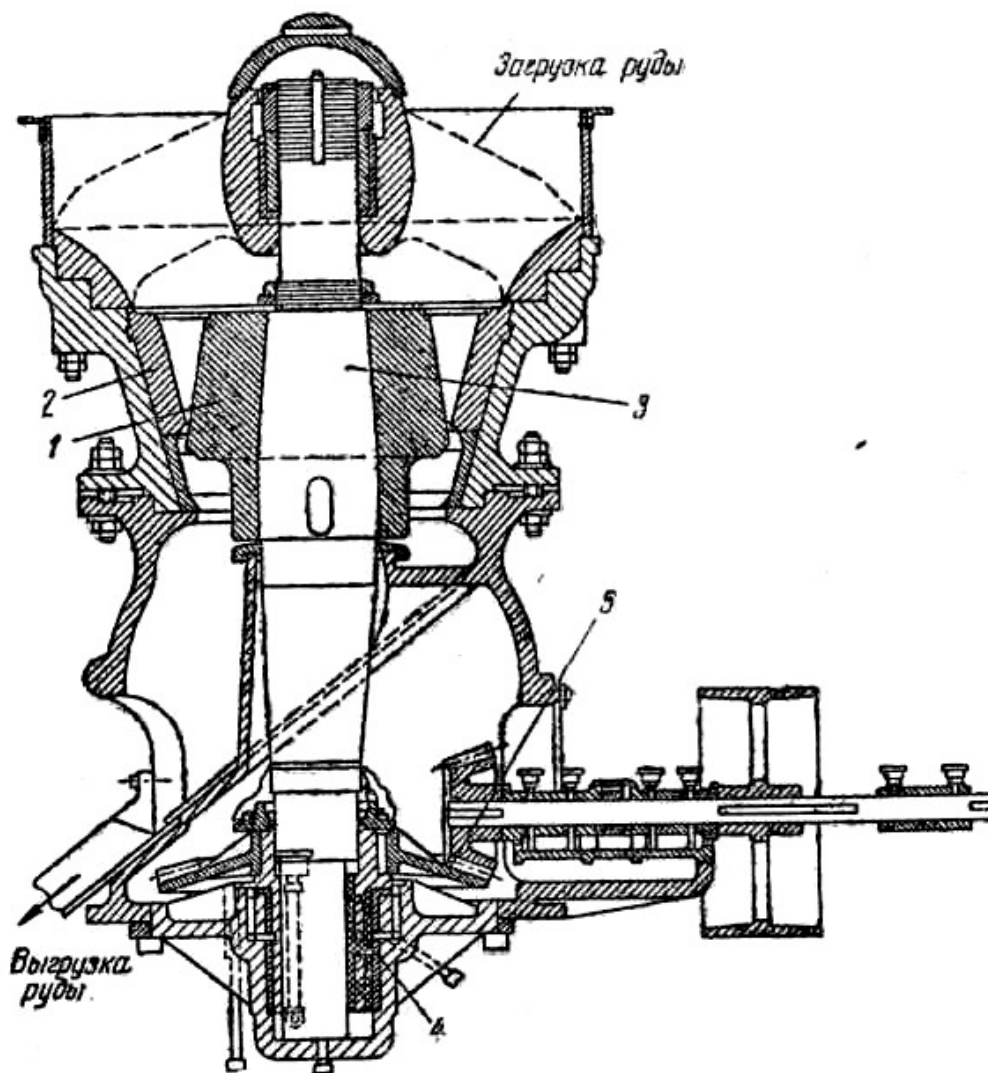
Конусная дробилка для крупного дробления: 1 – подвижный конус; 2 – неподвижный конус; 3 – вал; 4 – эксцентриковый стакан; 5 – зубчатая передача
